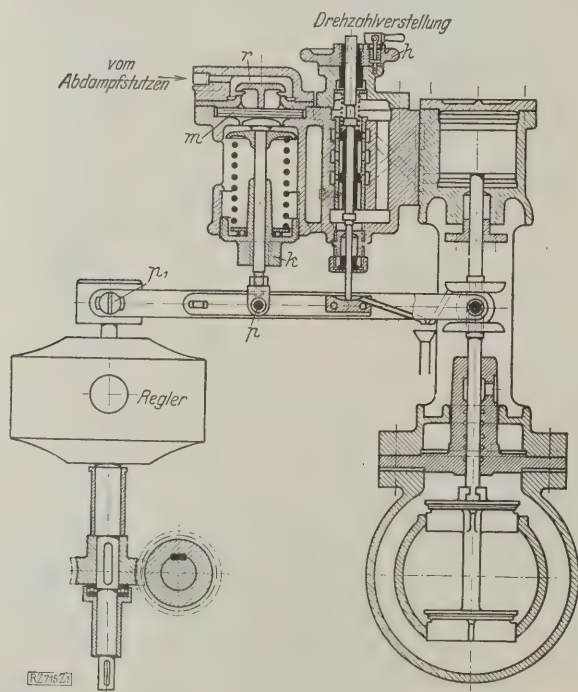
Steuerung mit Abdampfdruck-Regelung für Kleindampfturbinen.
